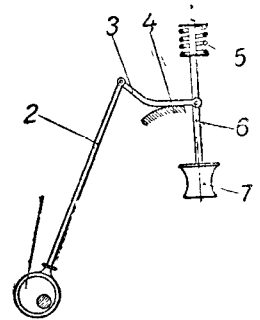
Парораспределительный механизм с катящимся рычагом.
